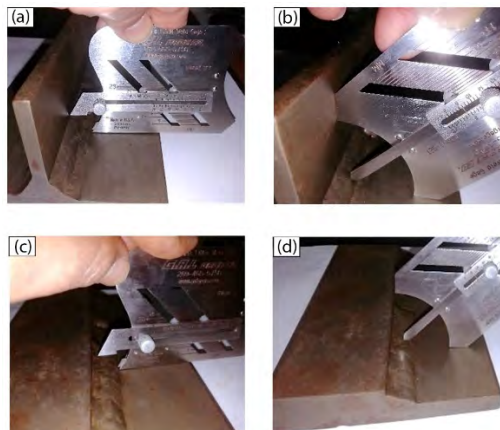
Disposición de Adjustable Fillet Weld Gauge para dimensionar el tamaño de (a) pierna en junta en T, (b) garganta en junta en T, (c) pierna en junta de solape y (d) garganta en junta de solape
